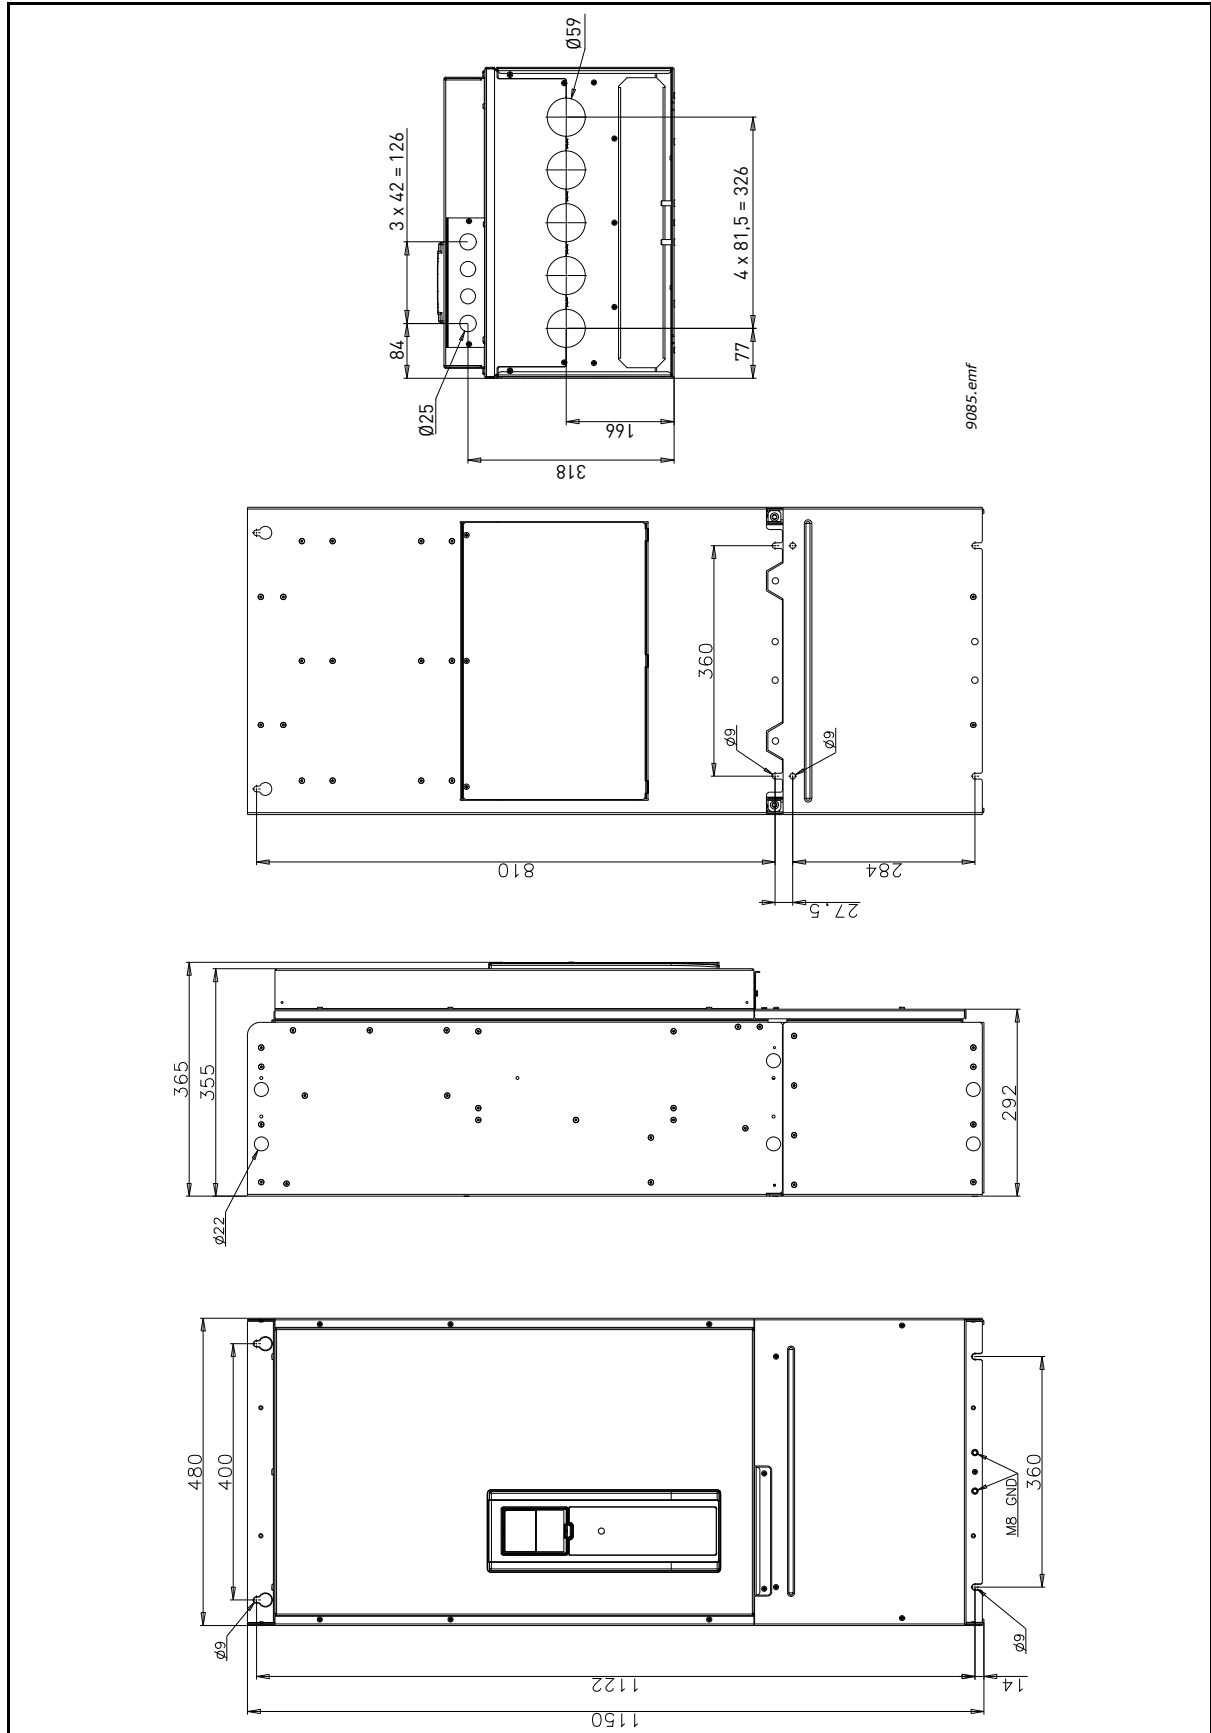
Dimensioner for Vacon-frekvensomformer, MR6, vægmontering
